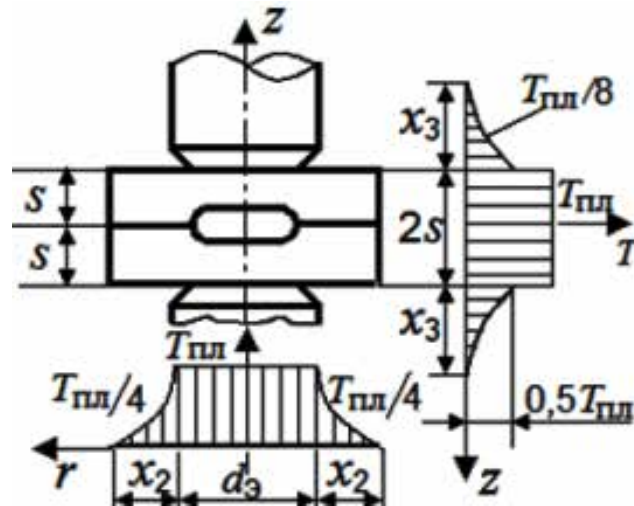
Розрахункова схема визначення сили зварювального струму
